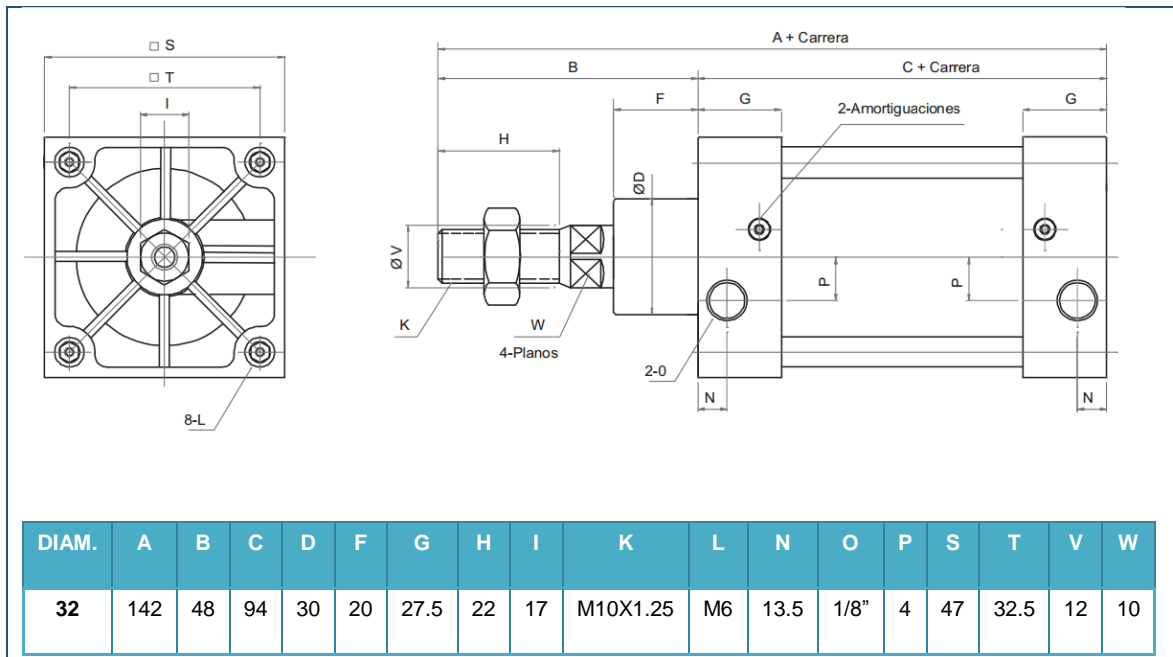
Dimensión del cilindro de 32mm de diámetro.
